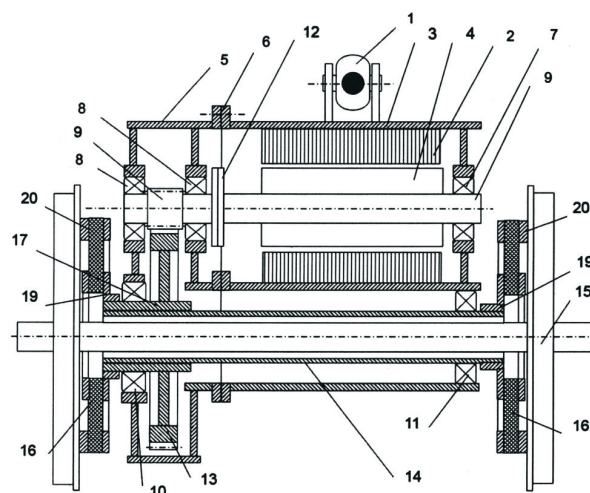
Опорно-центральный привод интегрированной схемы: 1 – подвеска; 2 – ТЭД; 3 – статор; 4 – ротор; 5 – осевой редуктор; 6 – разъемное соединение; 7 – подшипник ротора; 8 – подшипники вала осевого редуктора; 9 – вал осевого редуктора; 10, 11 – осевые подшипники; 12 – мембранная муфта; 13 – большое зубчатое колесо; 14 – полый вал; 15 – колесная пара; 16 – упругие элементы; 17 – ступица; 18 – секторы упругого элемента; 19 – фланец; 20 – кольцевой выступ
